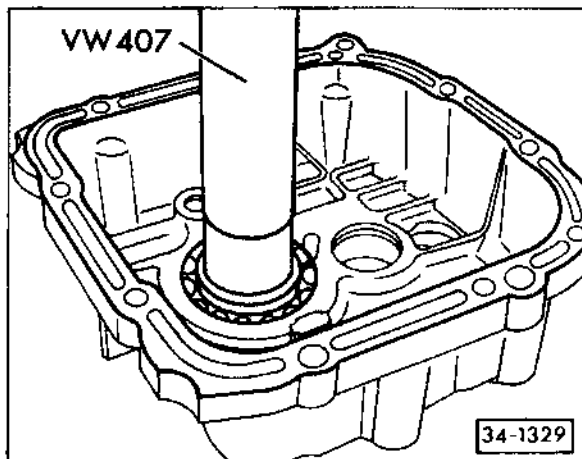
Rillenkugellager aus Lagerschild auspressen
